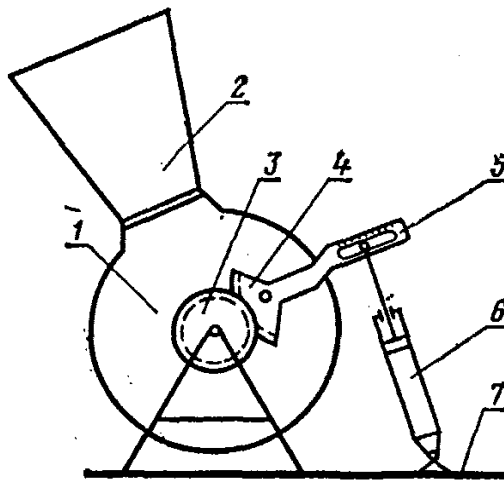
Схема механизма поворота распыливающего устройства:
